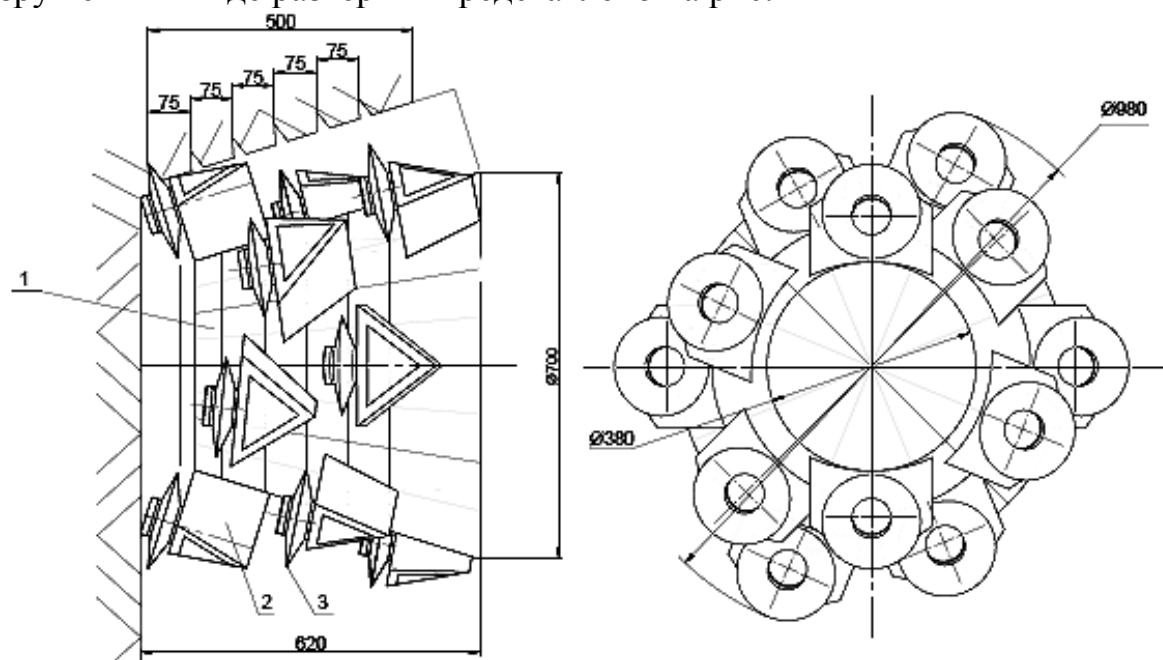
Конструктивная схема радиальной реверсивной коронки
